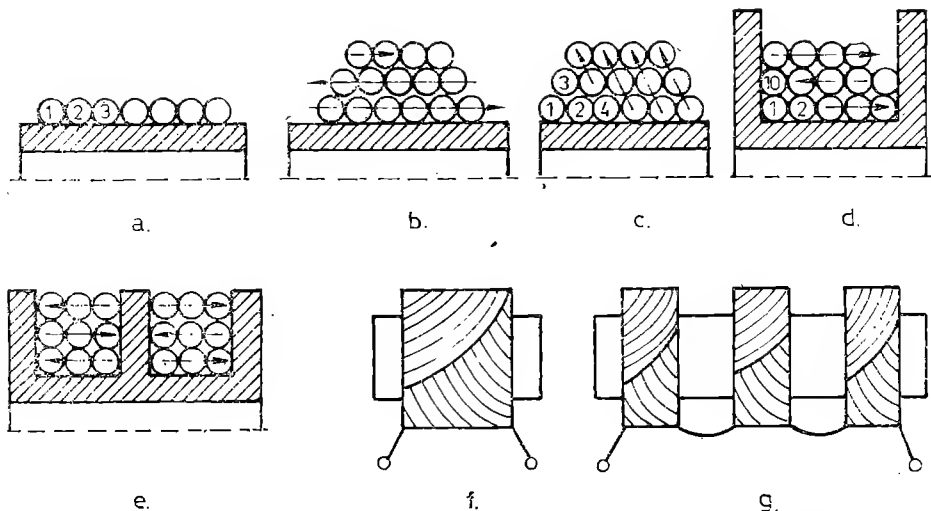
Tipuri de bobinaje: a) într-un strat; b) cilindric fără flanșe; c) piramidal; d) cilindric, pe carcase cu flanșe; e) bobinaj secționat; f) în fagure; g) fagure în găleți.
